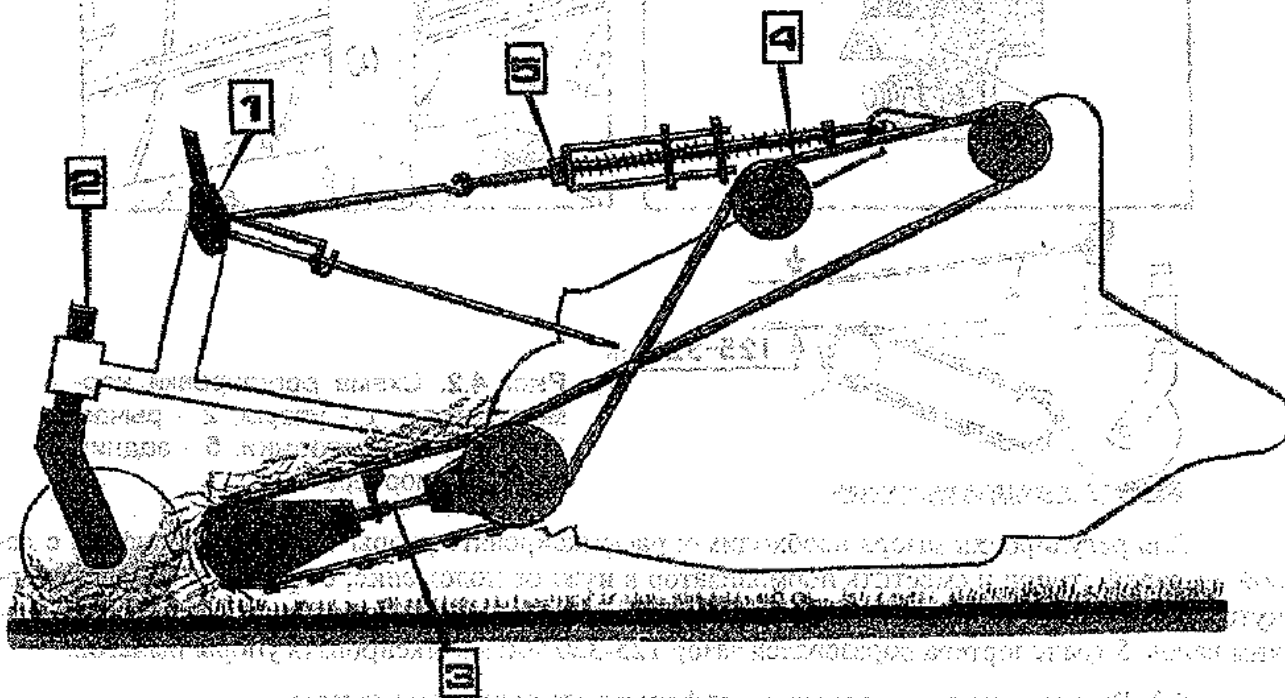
Схема платформы-подборщика: 1-нормализатор; 2- колеса опорные; 3-винт натяжения тяговых цепей транспортера; 4-ремень приводной; 5-разгружающее устройство
